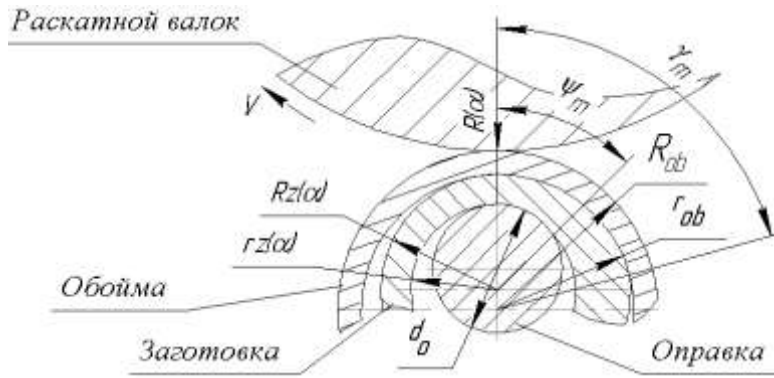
Схема взаимодействия раскатного вала, обоймы, заготовки и оправки
